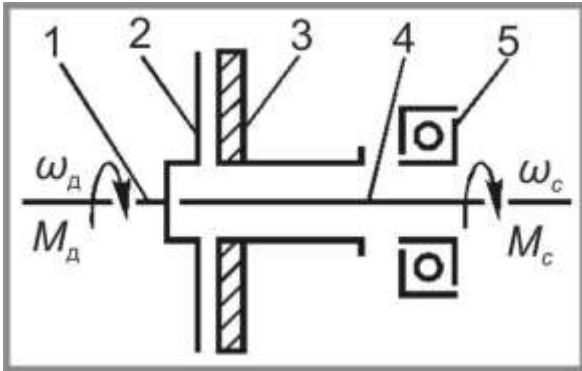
Принципова схема механічного фрикційного зчеплення: 1, 4 – ведучий і ведений вали; 2, 3 – ведучий і ведений диски; 5 – натискний підшипник
